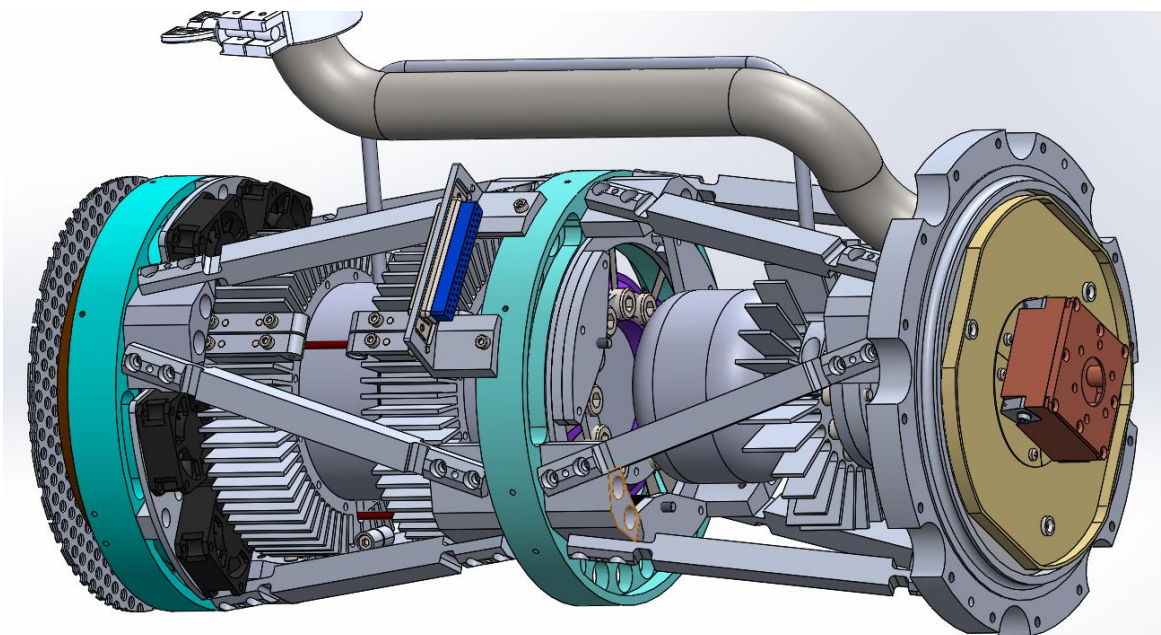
Vue du sous-ensemble cryocooler sans capotage
